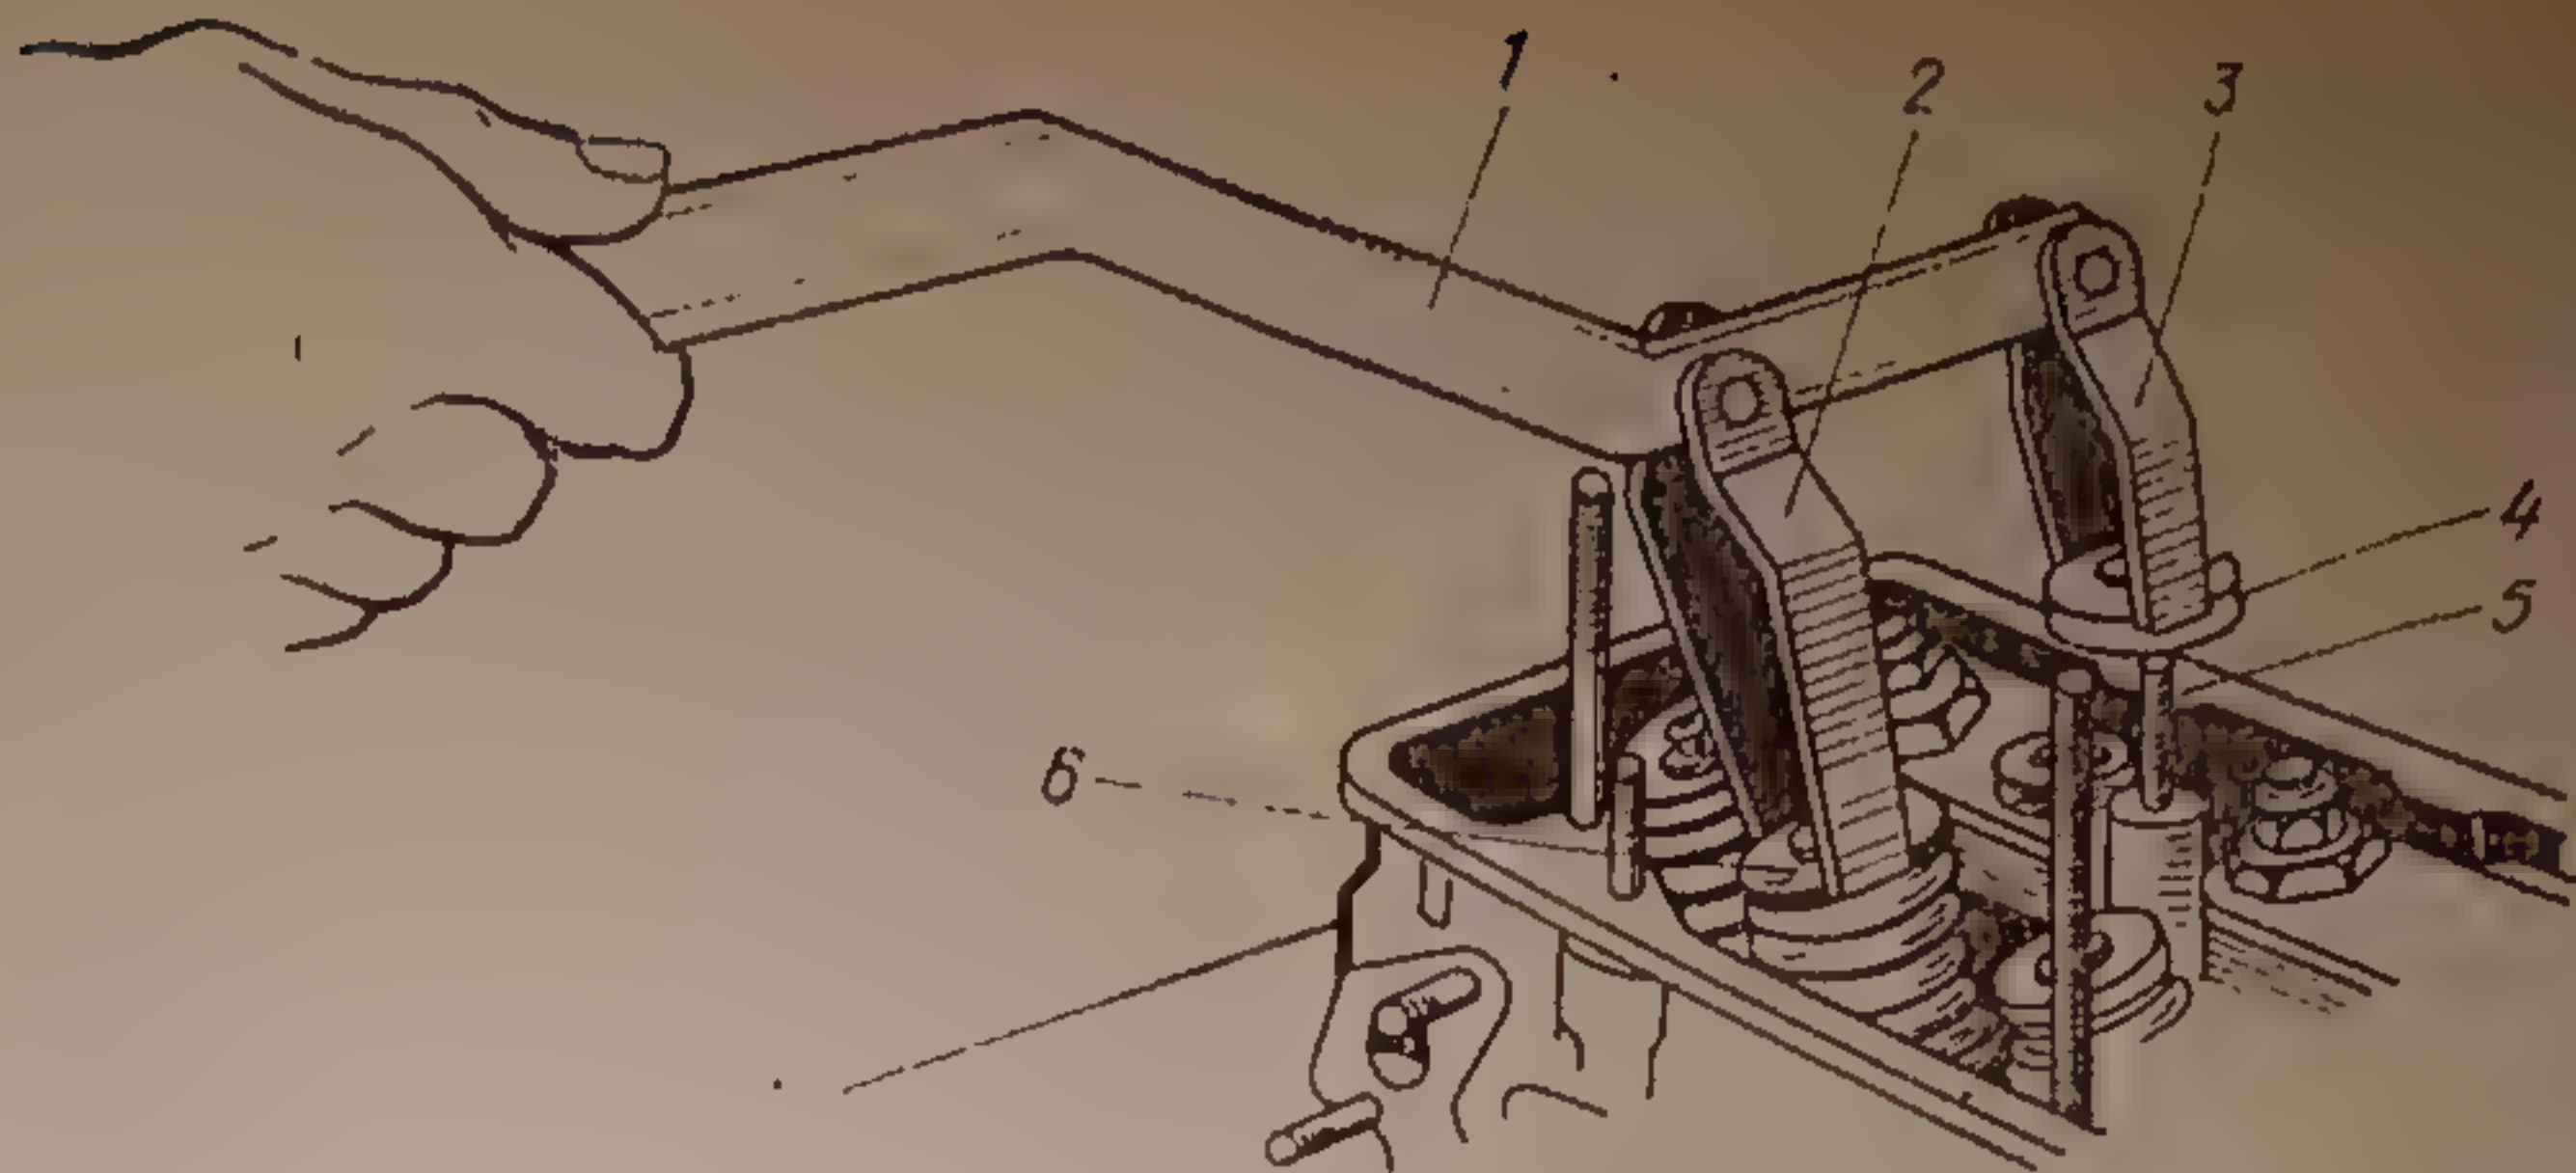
Приспособление для снятия пружин клапана двигателя: 1 — рычаг; 2 — опора, сжимающая пружину; 3 — упор, фиксируемый на шпильке; 4 — вилка шпильки; 5 — шпилька, крепящая корпус распределительного вала; 6 — опорный диск
